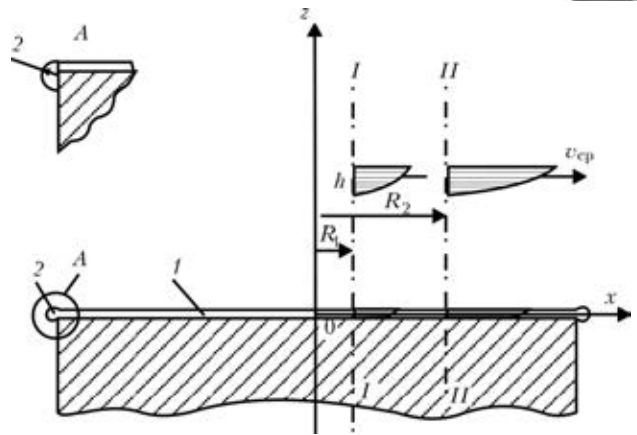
Сечение расходуемой заготовки: 1 — слой жидкого металла; 2 — кольцо металла на кромке заготовки; эпюры скоростей I-I; II-II; A — кромка заготовки
